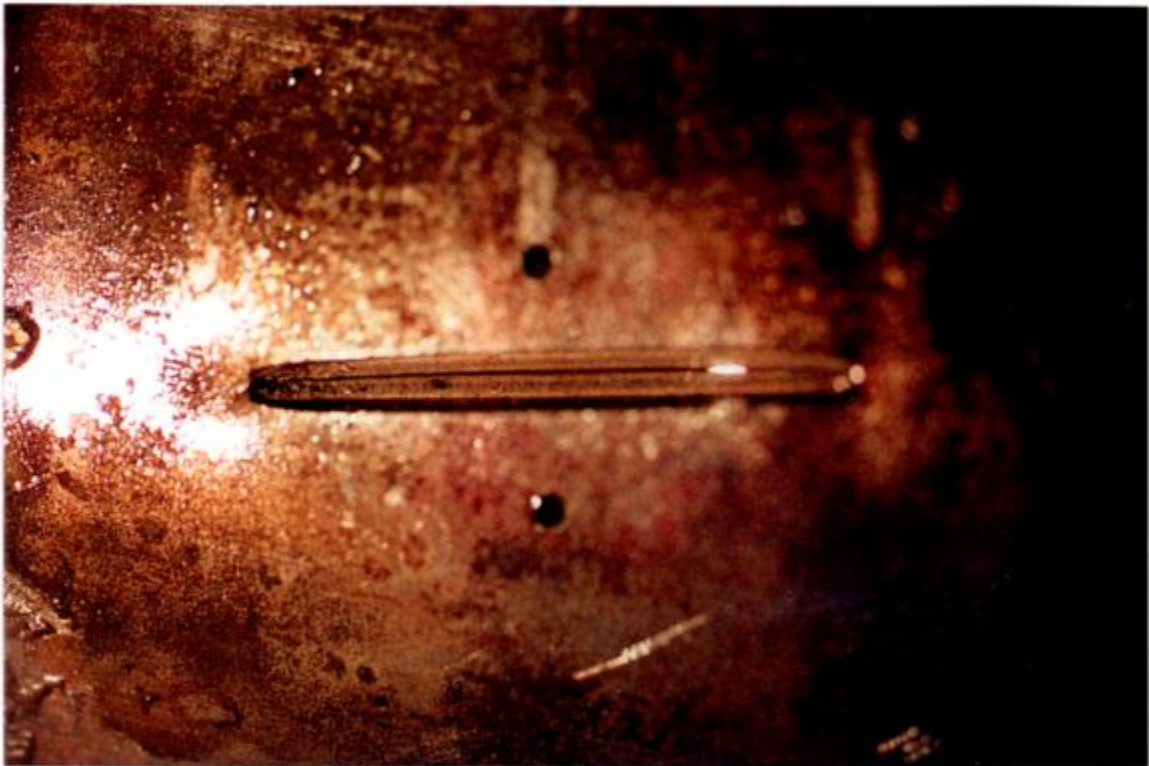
Aspecto de la fractura en la probeta 4 (tubo grado X65)
